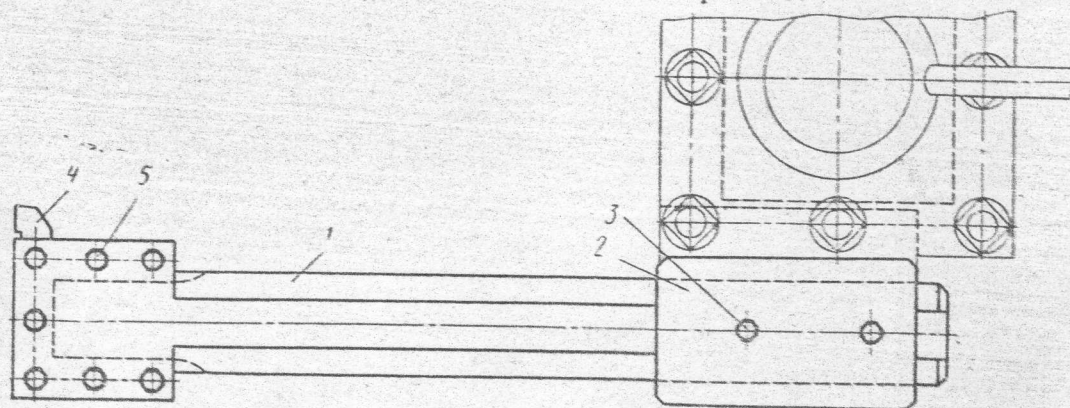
Резцовая оправка для обработки деталей над выемкой в станине
